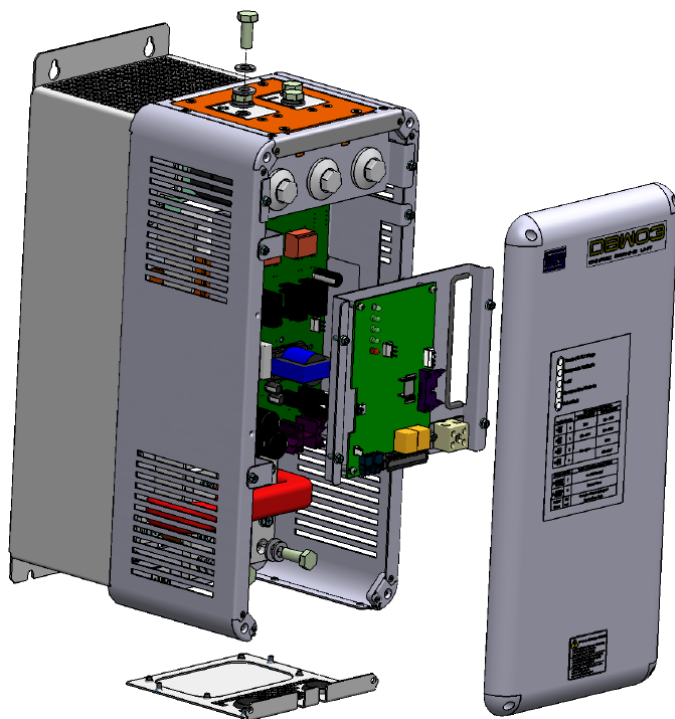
Principais componentes do módulo de frenagem DBW03
